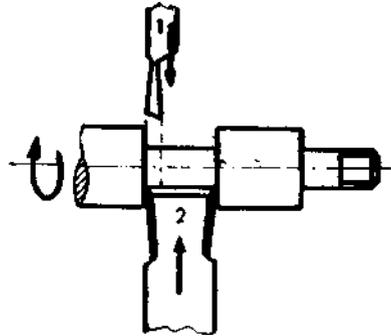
La herramienta de tronzar (1) iniciará el corte en el diámetro torneado por la herramienta (2)
